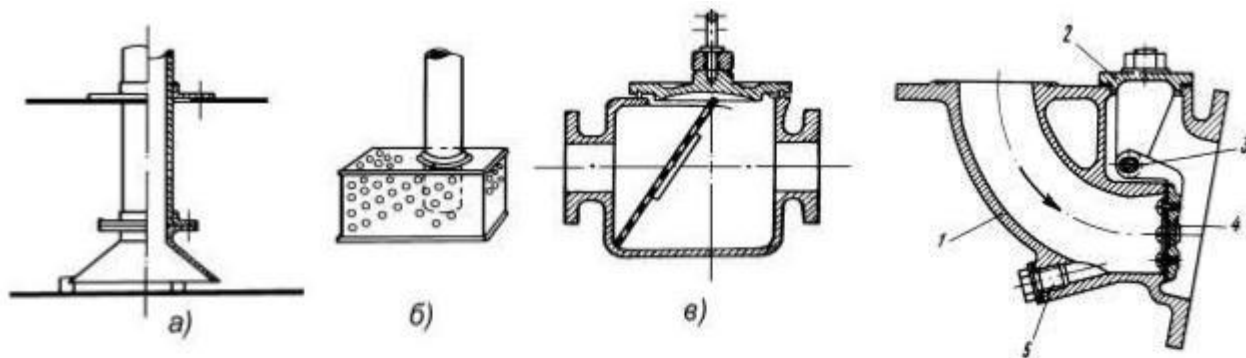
Приемные отростки и грязевые решетки Рисунок 5.8 - Захлопка бортовая и коробка. 1 –корпус;2–крышка;3 – валик;4 – тарелка; 5 – пробка спускная
